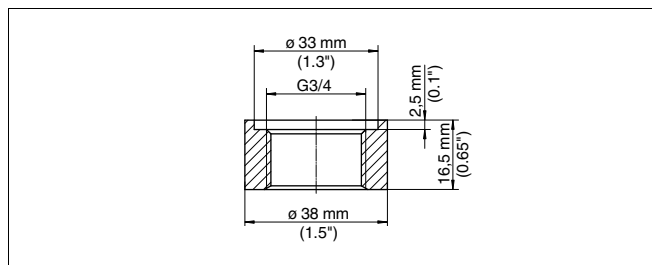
Medidas da luva soldada G $\frac{3}{4}$ A conforme DIN 3852-X
